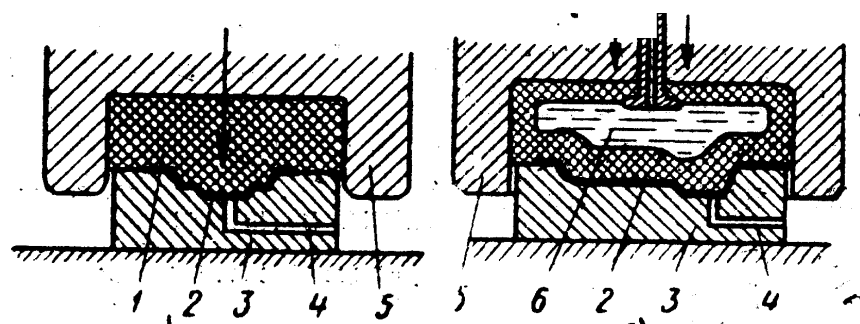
Схемы штампов для формовки резиной пространственных деталей
